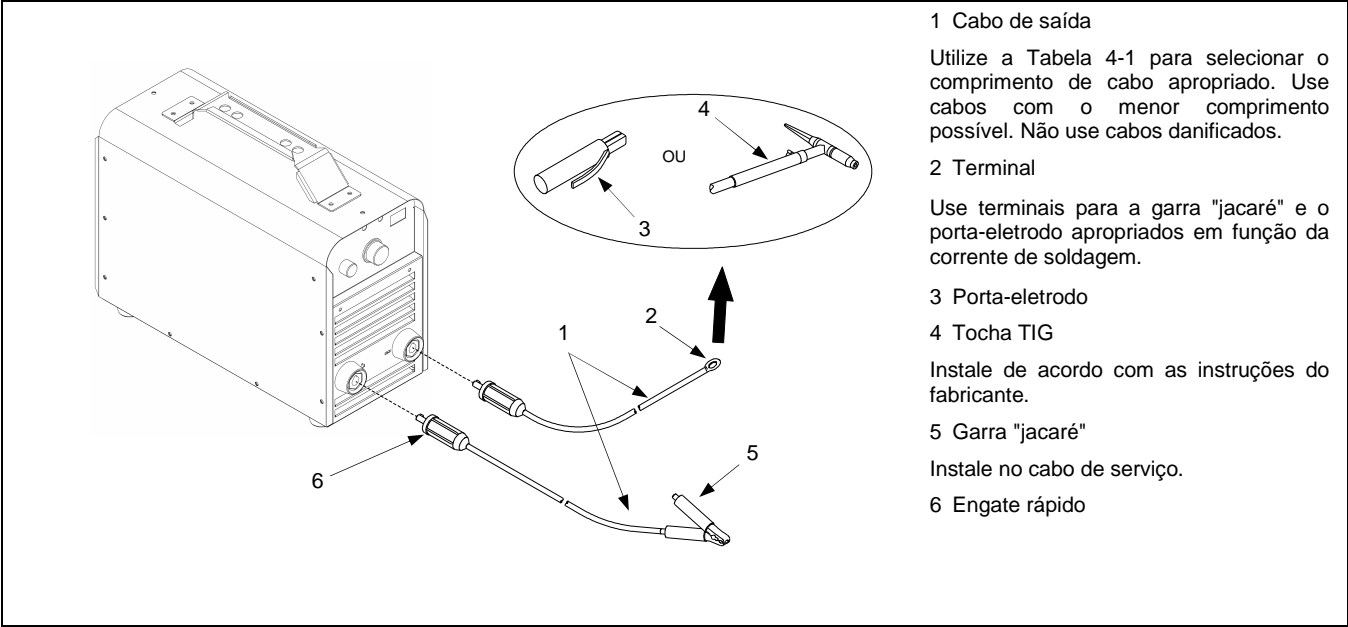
Escolha e preparação dos cabos para a soldagem
